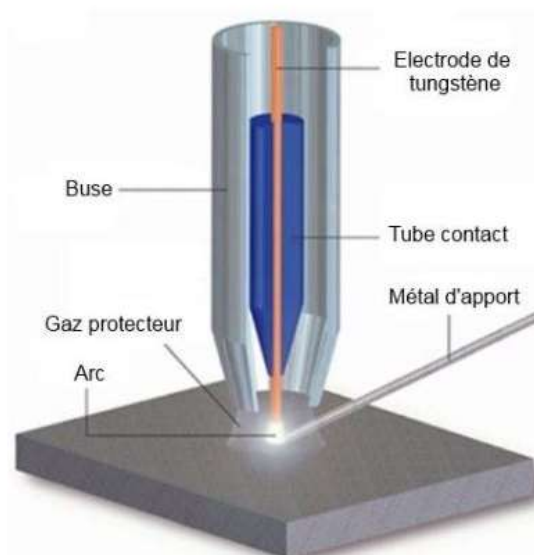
3 Le procédé de soudage GTAW [21].
